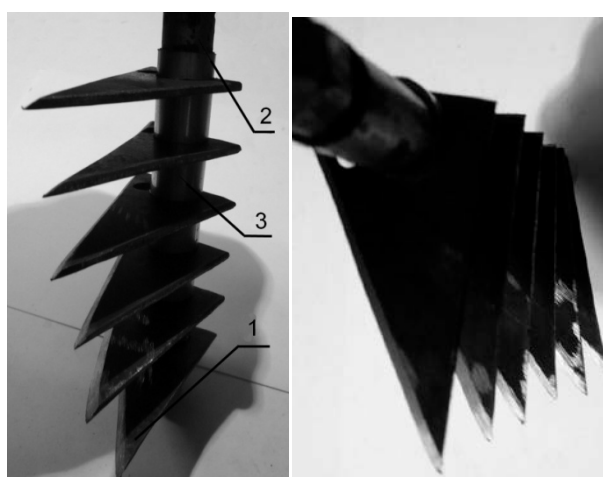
Схема расположения ножей в блоке: 1 – нож; 2 – ось блока ножей; 3 – шайба
